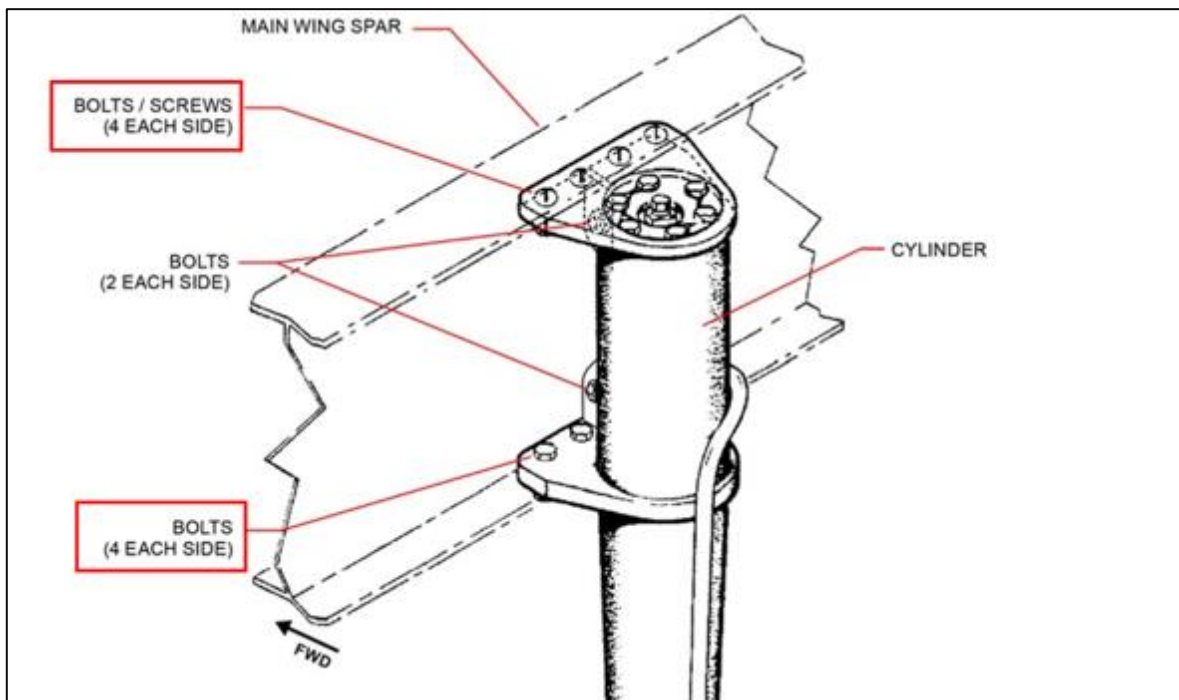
Diagrama de la zona de fijación del tren de aterrizaje al plano.
